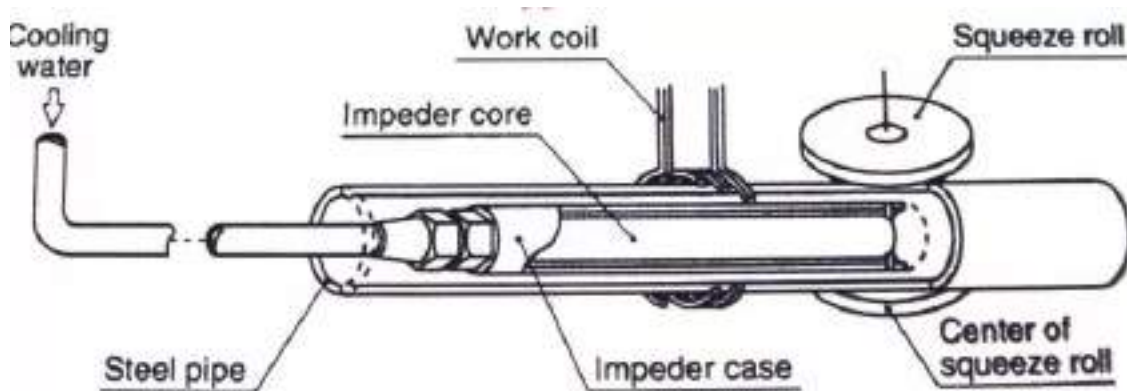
Representación de soldadora continua del tipo “ERW”(Electric Resistive Welding):
